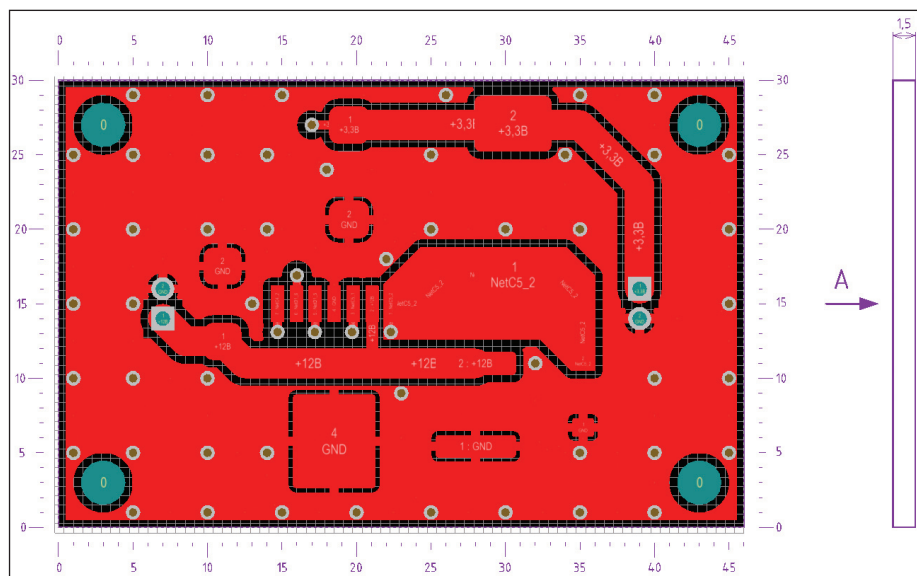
Сформированные в Altium Designer вид сверху и вид сбоку чертежа печатной платы
